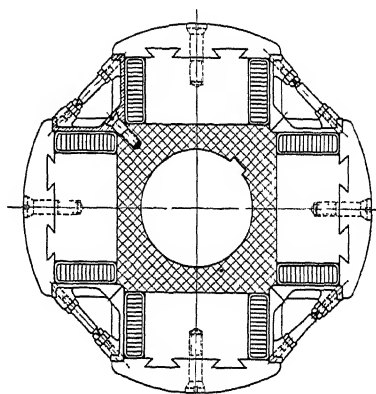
E.-A.-G. vorm. Kolben & Co., Prag.
